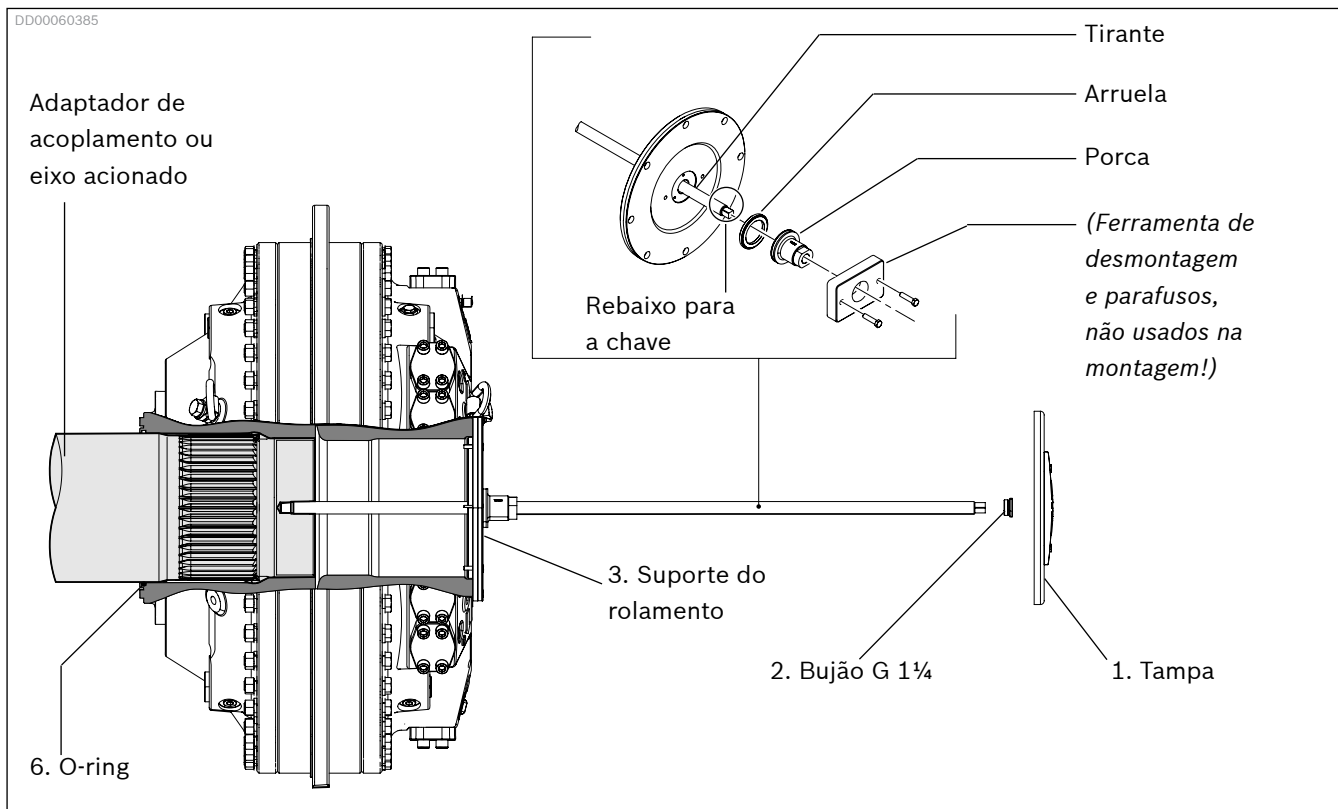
Montagem do motor com estria com a ferramenta de montagem
